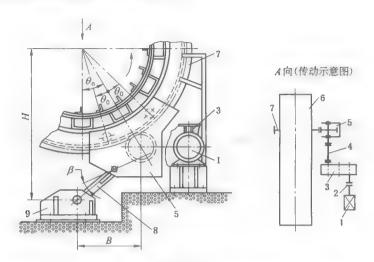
1—电动机; 2—联轴器(或液力偶合器); 3—初级减速器; 4—万向接轴; 5—悬挂小车; 6—简体; 7—大齿轮圈; 8—拉压杆; 9—支座
